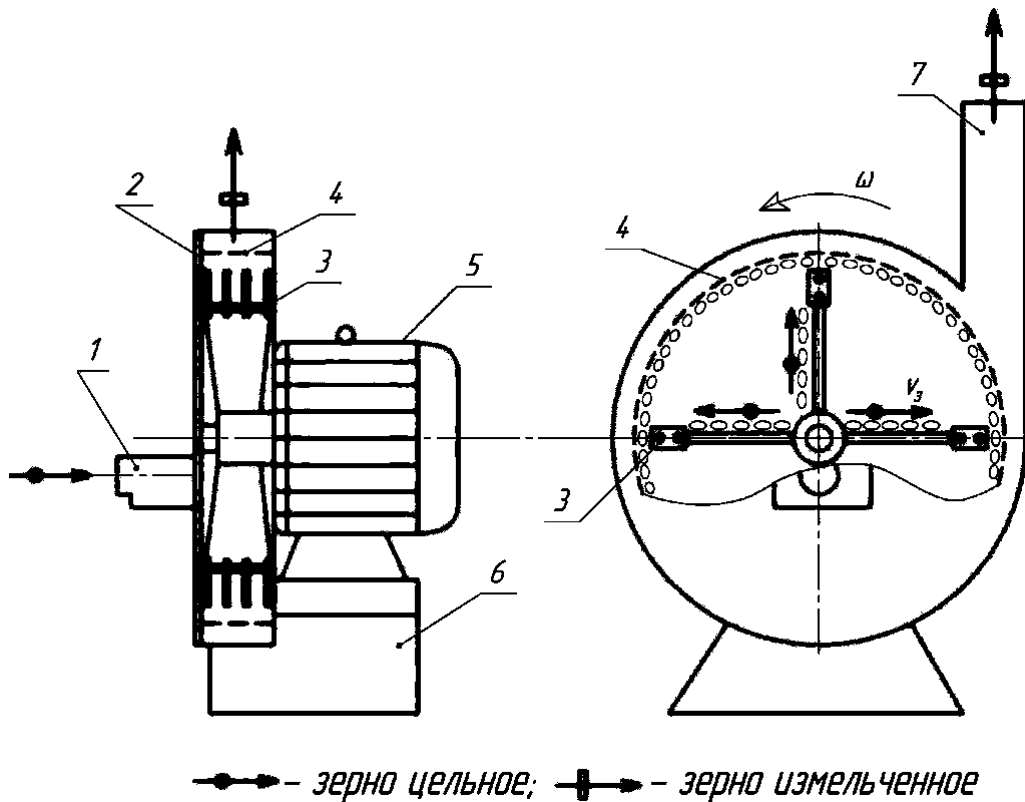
Схема работы всасывающе-нагнетательной дробилки: 1 – всасывающий патрубок с металло-камнеуловителем; 2 – дробильная камера; 3 – дробильный барабан с шарнирно-подвешенными молотками; 4 – решето (сепаратор); 5 – электродвигатель; 6 – рама; 7 – нагнетательный патрубок
